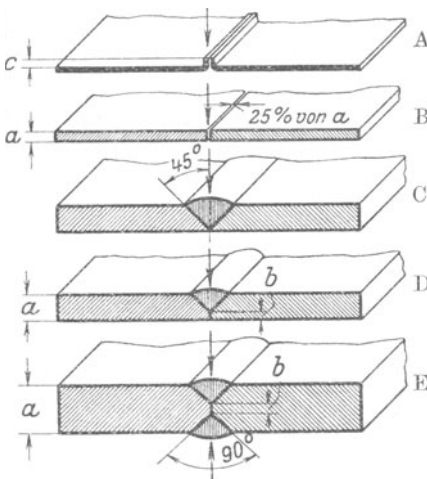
Vorbereitungsarbeiten bei Blechschweißungen.
